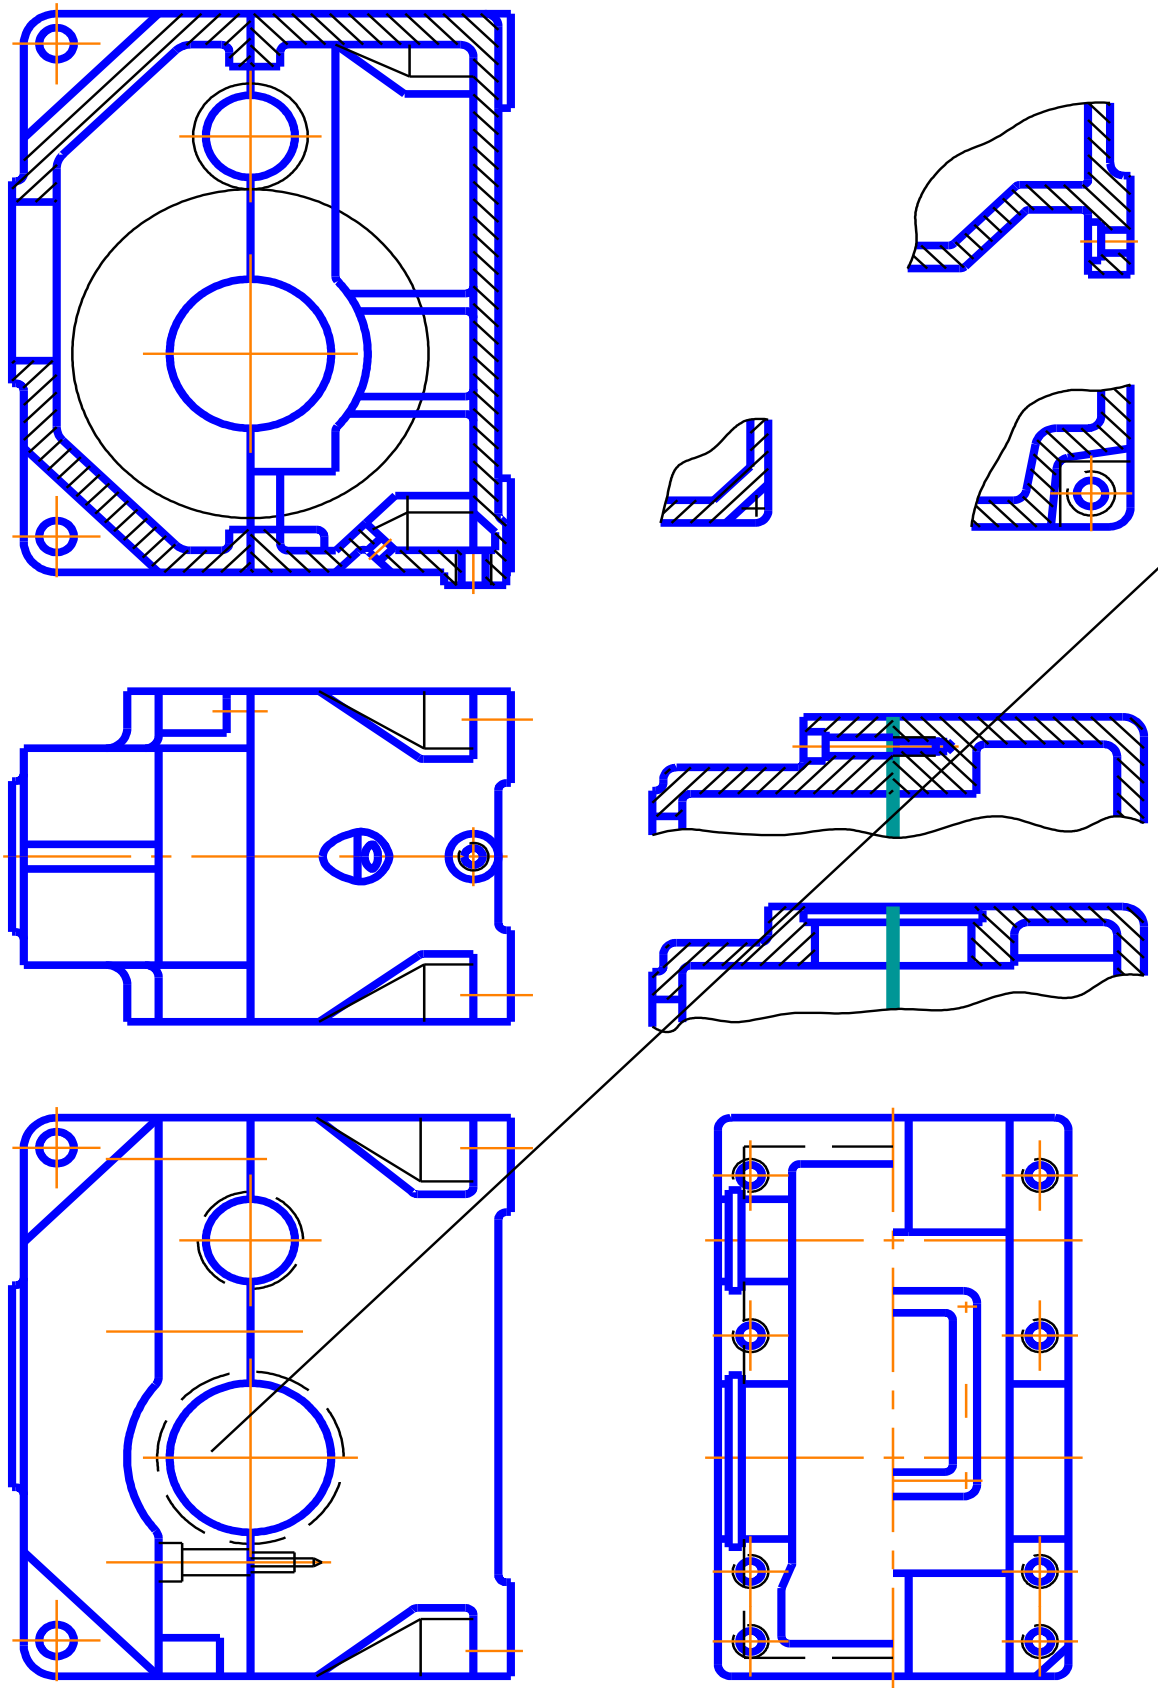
Корпус та його конструктивні елементи одноступінчастого циліндричного горизонтального редуктора з розташуванням виступаючих елементів на внутрішніх поверхнях
